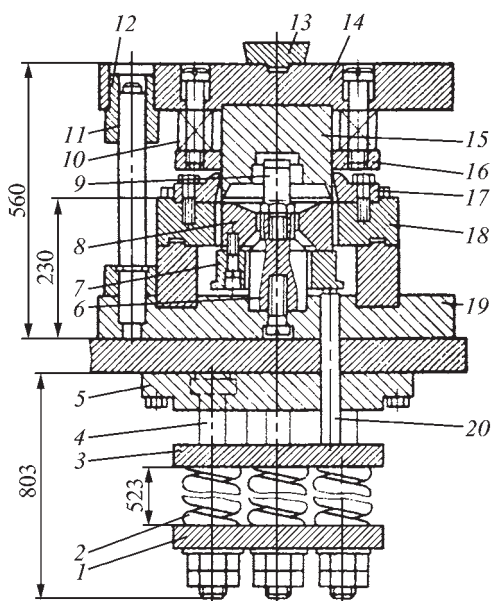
Совмещенный штамп с пружинным буфером для одновременной обрезки, пробивки и правки:
